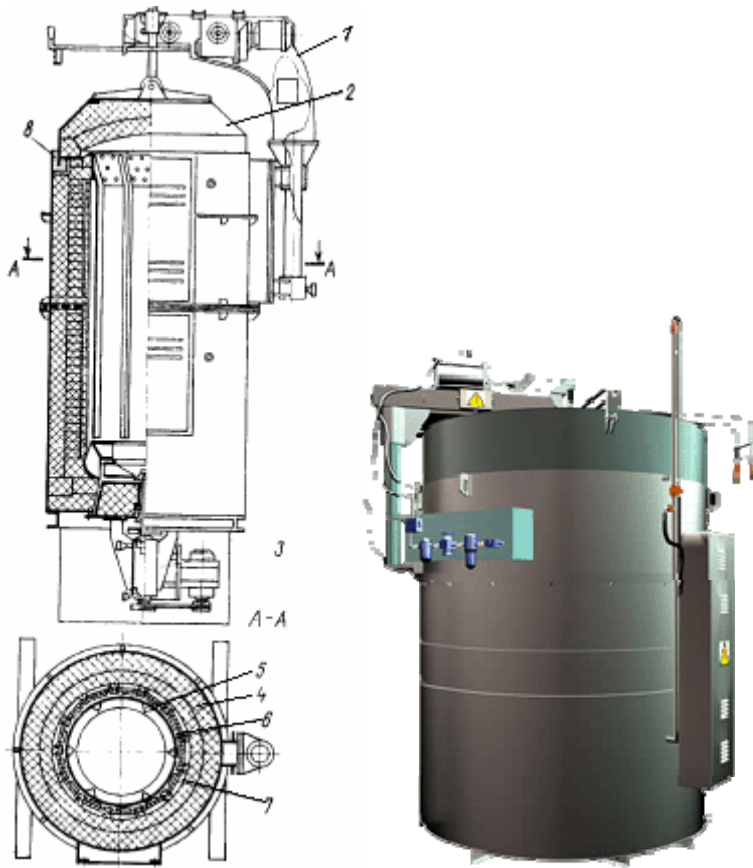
Шахтная электропечь: 1 – механизм подъема и поворота крышки; 2 – крышка; 3 – вентилятор; 4 – футеровка; 5 – направляющие; 6 – экран; 7 – нагреватели; 8 – песочный затвор
